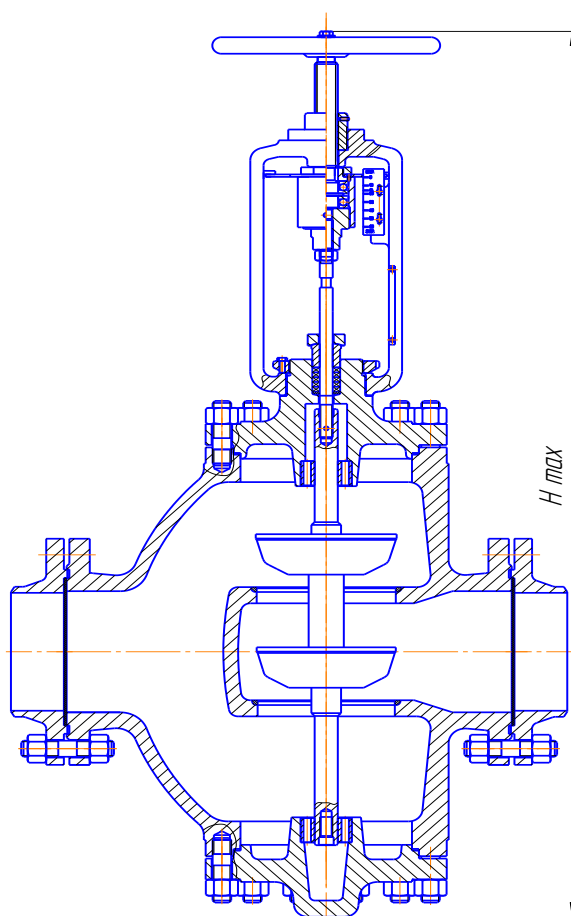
Клапан регулирующий КРД 65235 с РП
